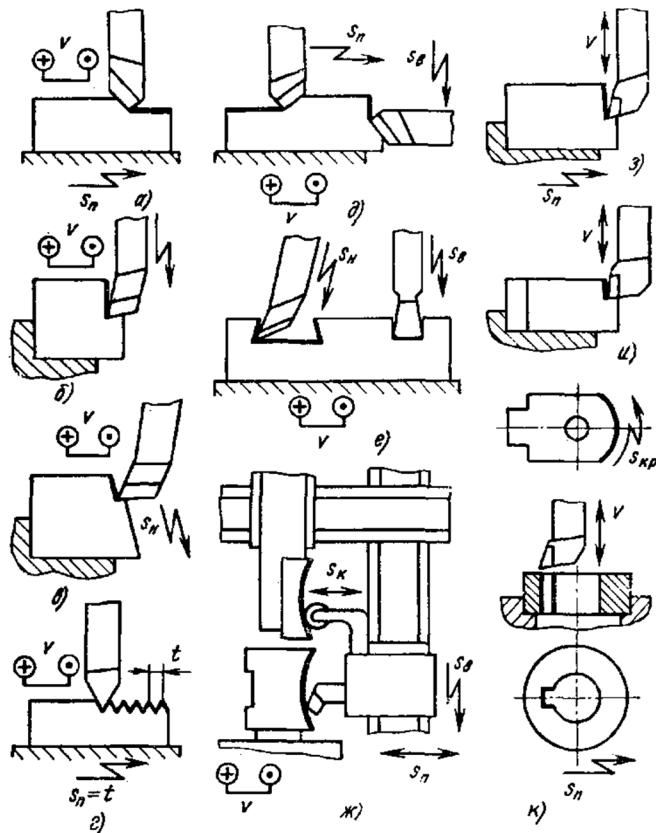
Схемы обработки поверхностей заготовок на строгальных и долбежных станках
